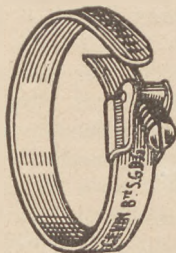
Schraube als Schneckengetriebe wirkend, beim Spannen
